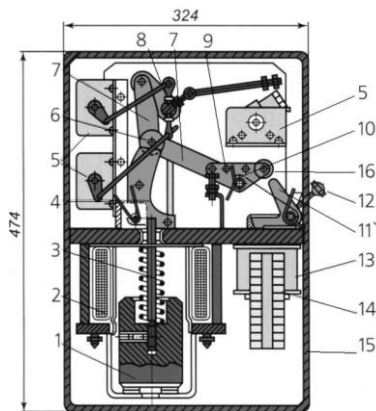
Электромагнитный привод ПЭ-11: 1, 2 - соответственно сердечник и катушка включающего электромагнита; 3 - шток; 4 - удерживающая защелка; 5 - блок - контакты КСА; 6 - ролики; 7 - серьги; 8 - вал; 9 - треугольный рычаг; 10 -
